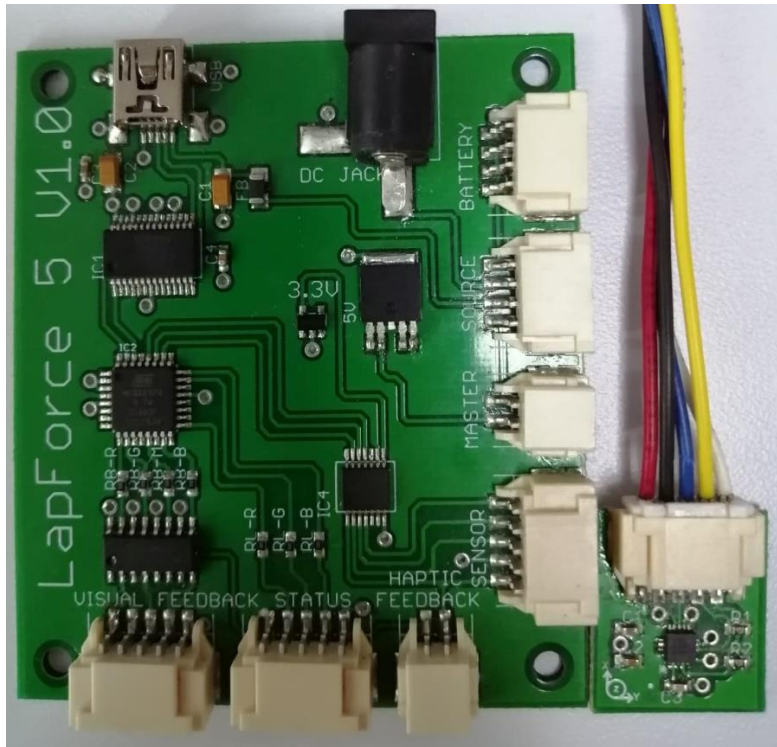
Vista frontal del PCB del sistema SurgForce y el MMA8451Q.
